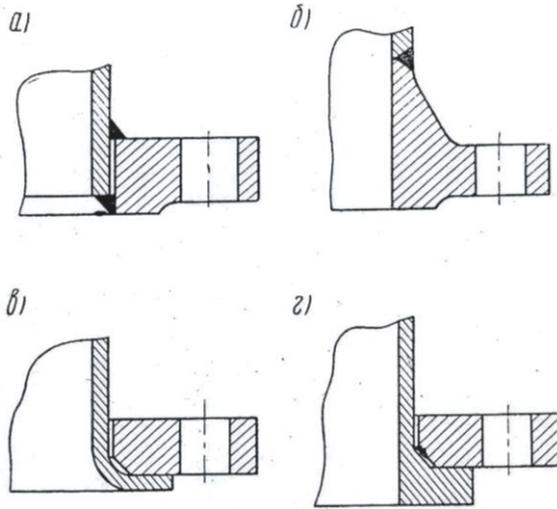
Типы фланцев: а – плоский приварной; б – приварной с шейкой; в – свободный на отбортовке; г – свободный на бурте
